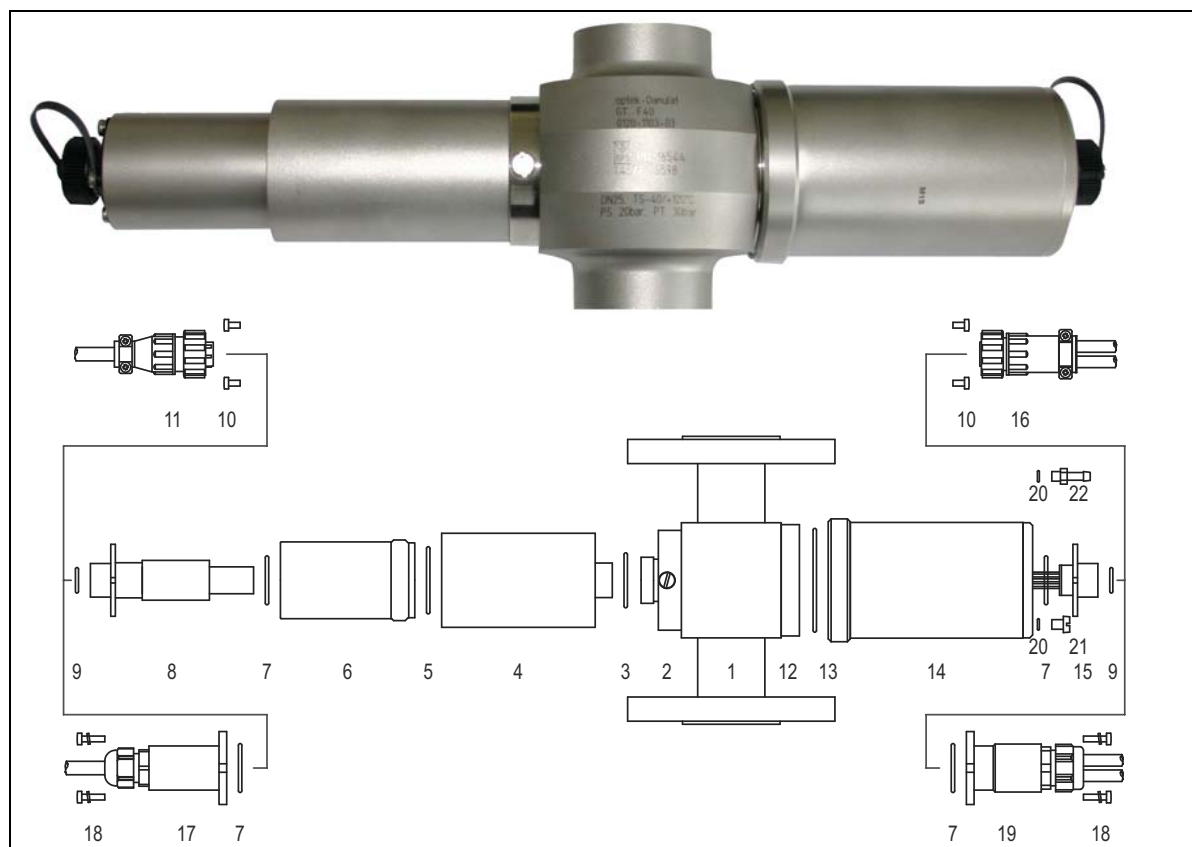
Foto y dibujo de despiece del sensor TF16 / TF16-N
